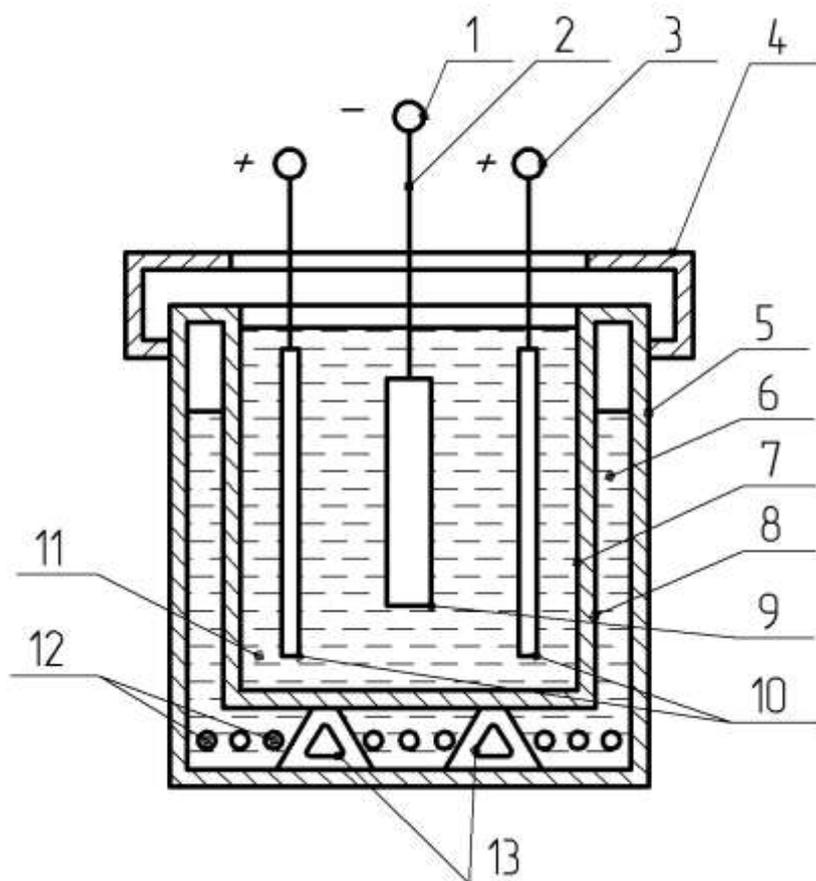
Ванна для нанесения гальванических покрытий: 1 и 3 – катодная и анодная штанги; 2 – подвесное приспособление; 4 – вентиляционный отсос; 5, 7, 8 – кожух, футеровка и корпус ванны; 6 – вода; 9 – катод (деталь); 10 – анодные пластины; 11 – электролит; 12 – подогрев ванны
